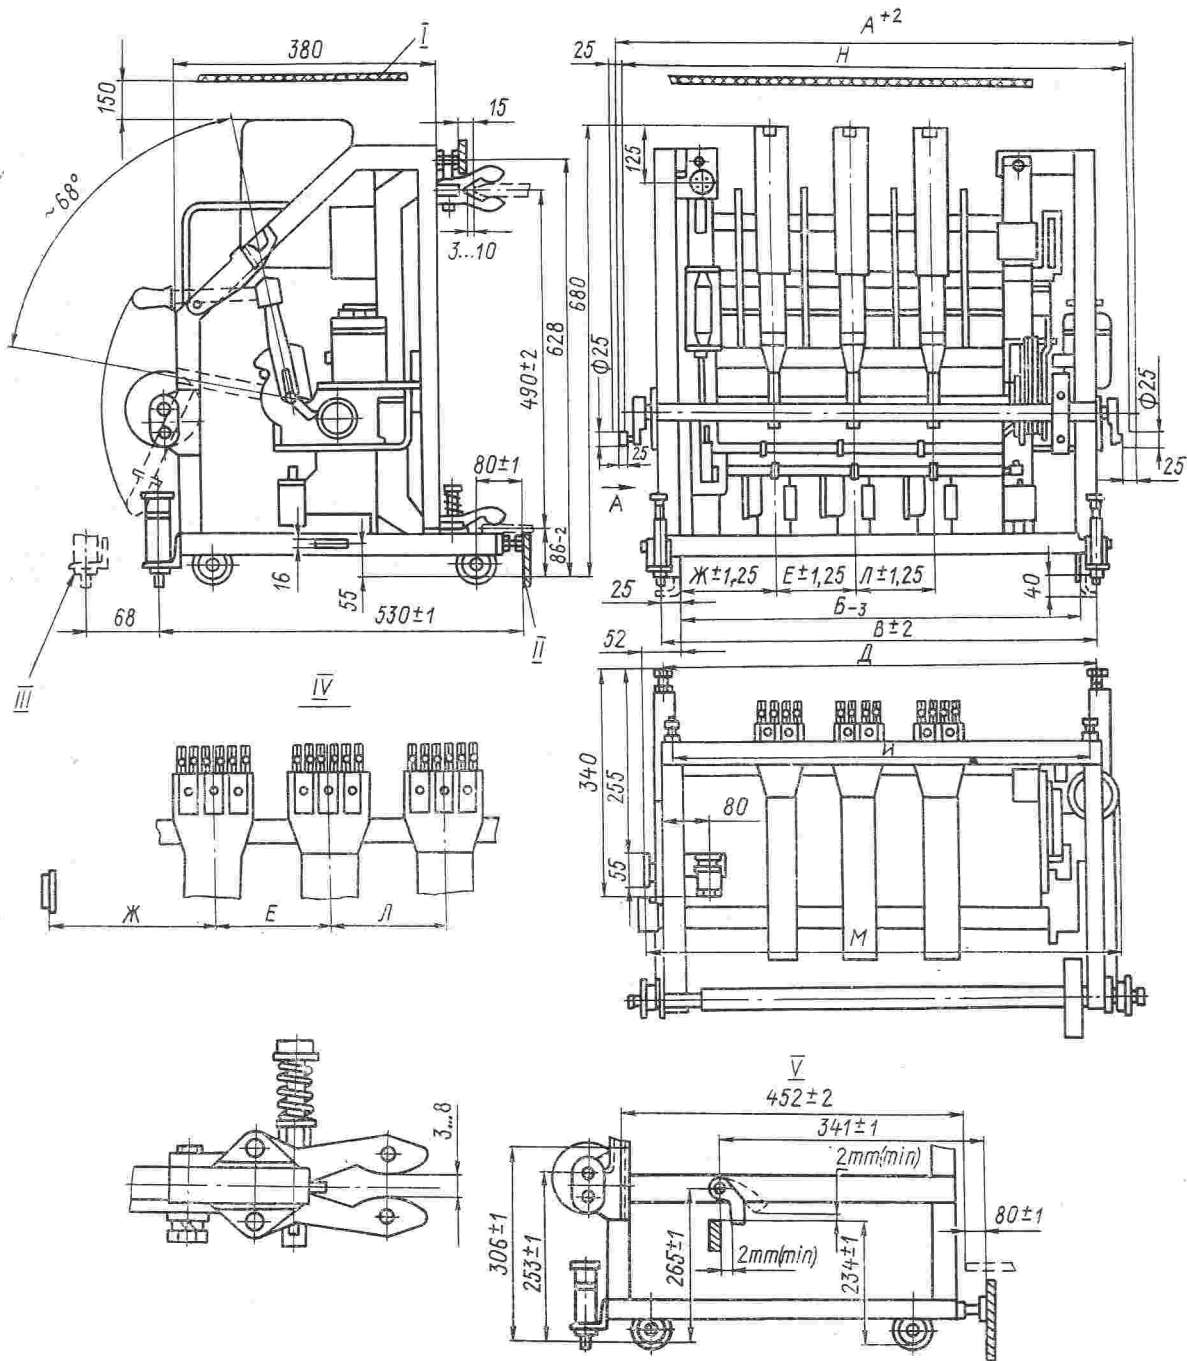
Габаритные и установочные размеры выдвижных выключателей с электродвигательным приводом:
